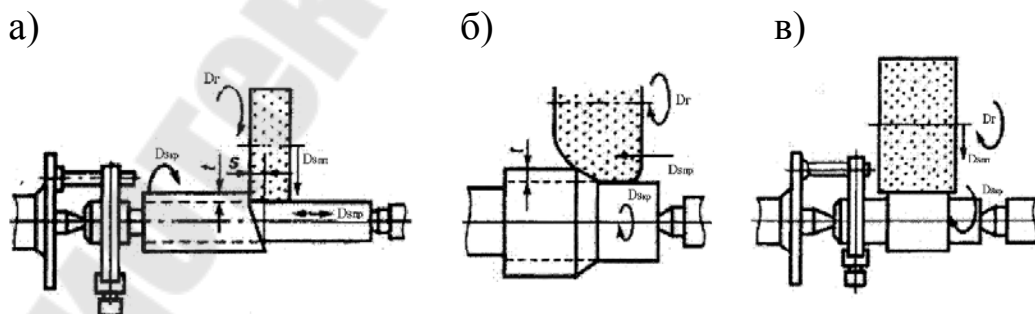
Схемы обработки на центровом круглошлифовальном станке
